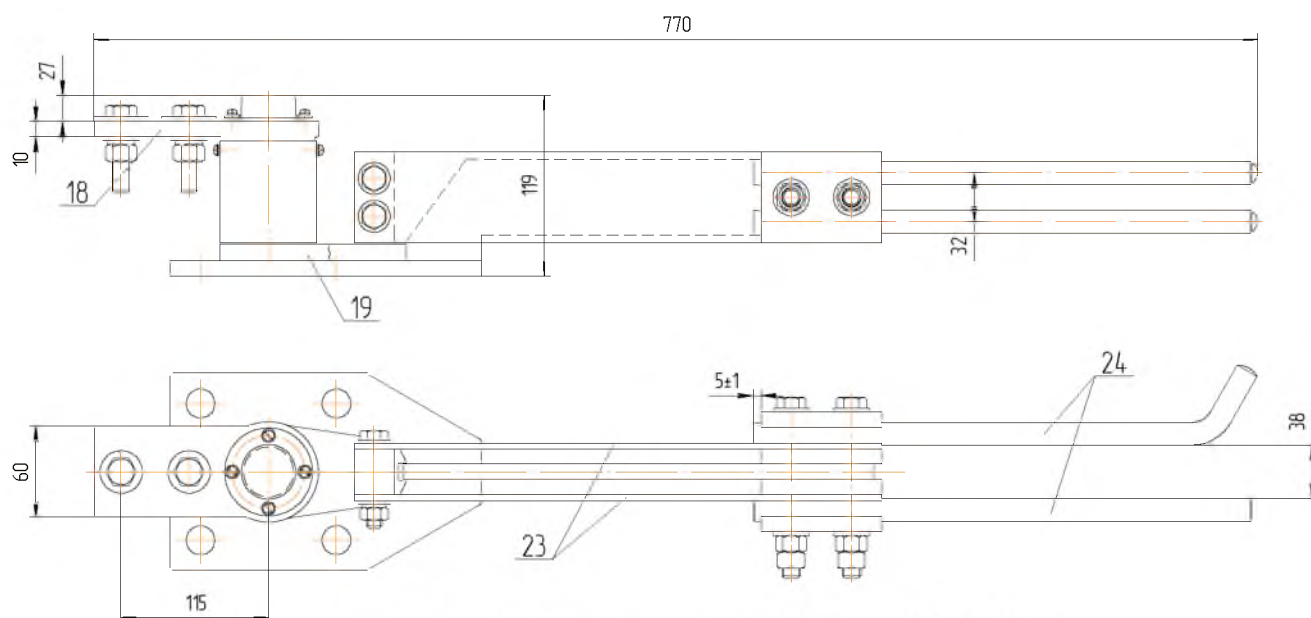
Нож контактный для РГП СЭЦ<sup>®</sup>-110/1250
